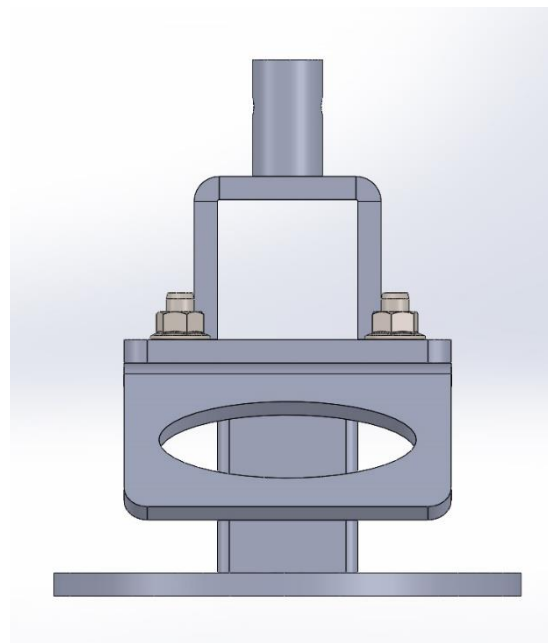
CAD-Konstruktion Radmotorenaufnahme Draufsicht
